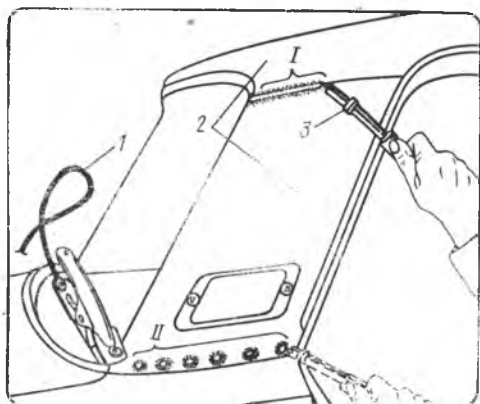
Сварка деталей кузова автомобилей ВАЗ в углекислом газе:
